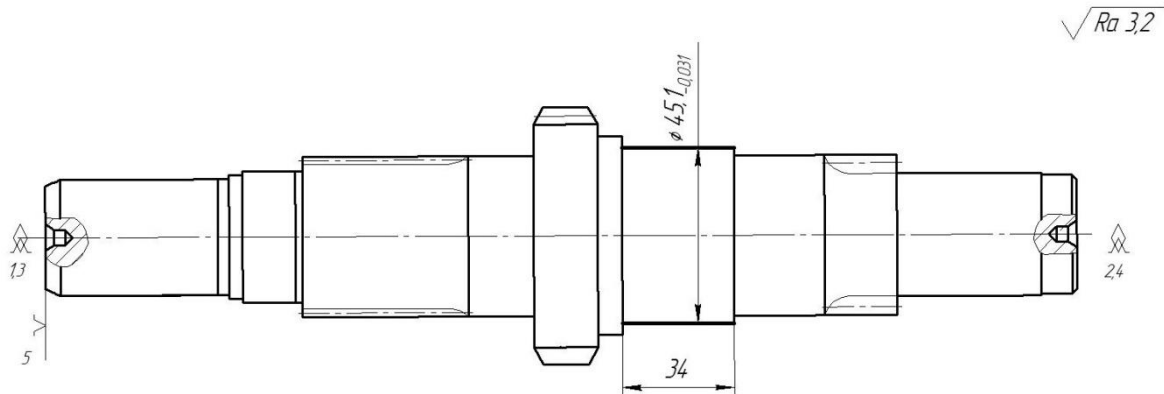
Схематичне відображення етапу фрезерування шліцьової частини вторинного вала КПП Ford Explorer.
